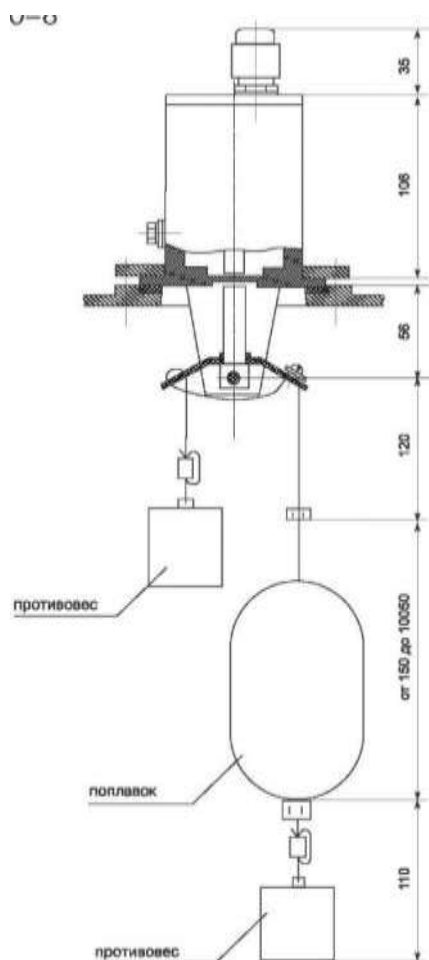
Габаритные и присоединительные размеры РОС 400-8
